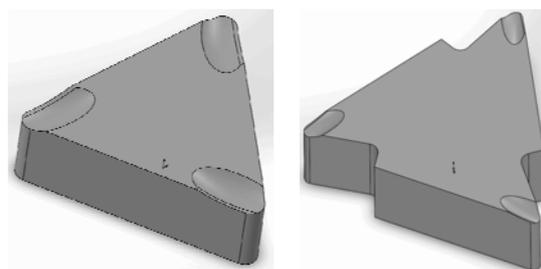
3D-модели твердосплавных пластин TNMR 160408 и TNMR 160404 для черновой и чистовой обработки нержавеющей стали
